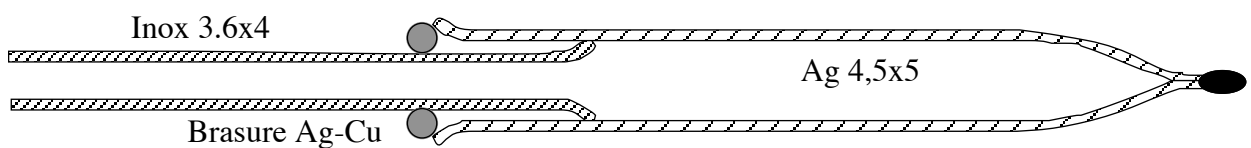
Dessin de la soudure expliquée dans le texte ci-dessus.
